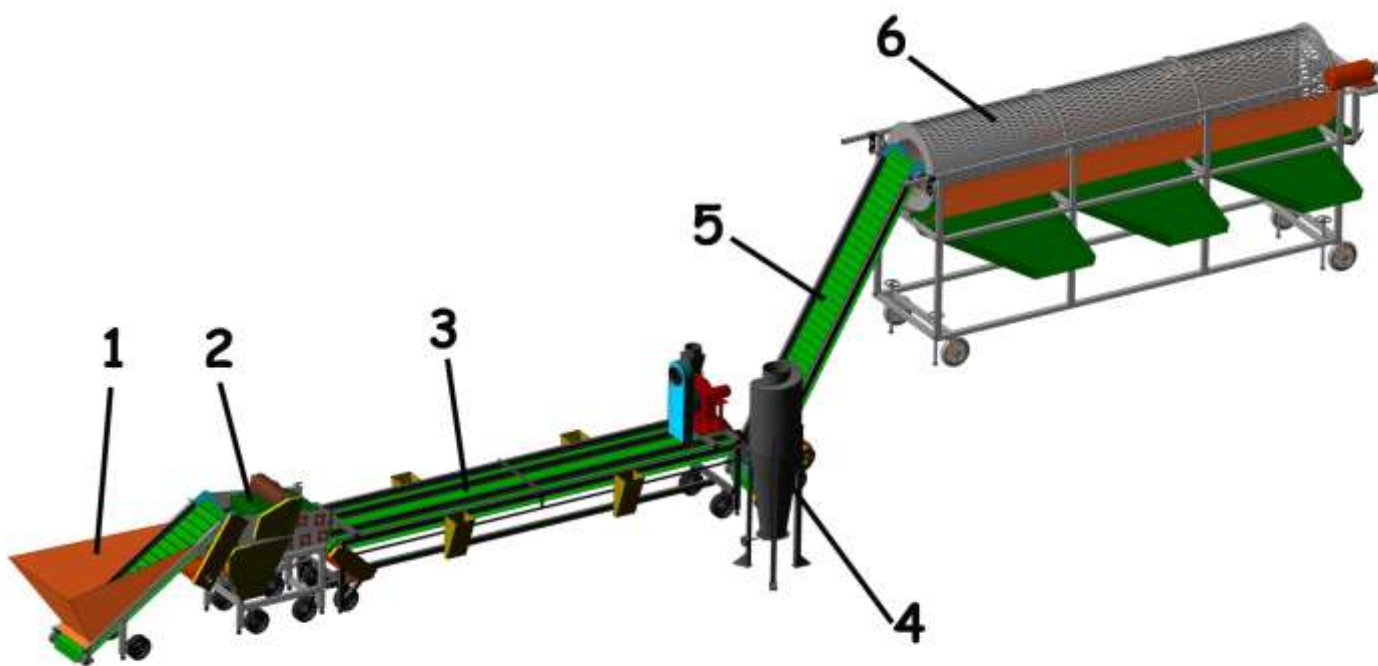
Линия подготовки чеснока ЛПЧ.
